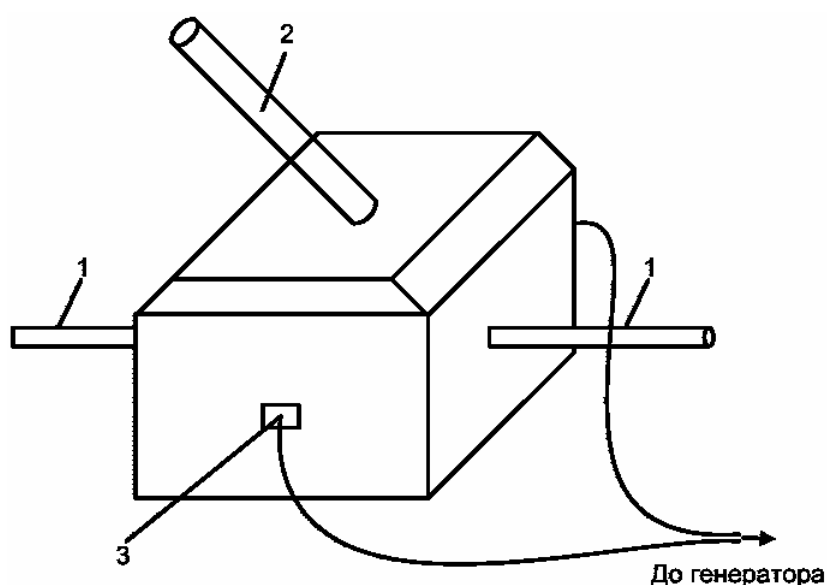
Загальний вигляд електрозварювального пристрою:
